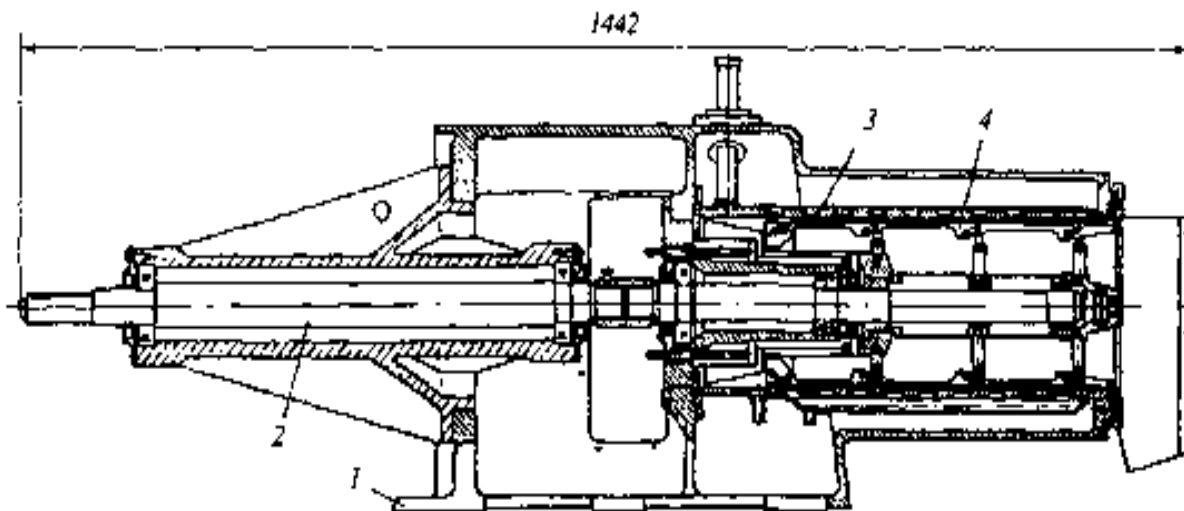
Общий вид сбивателя маслоизготовителя марки А1-ОЛО/1:
